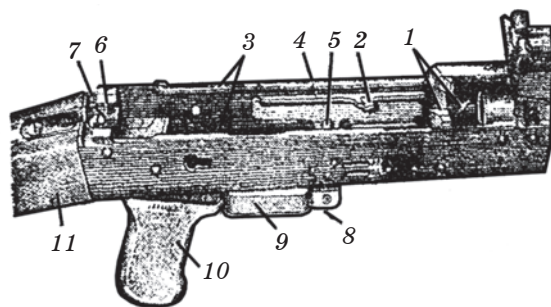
Ствольная коробка: 1 — вырезы; 2 — отражательный выступ; 3 — отгибы; 4 — направляющий выступ; 5 — перемычка; 6 — продольный паз; 7 — поперечный паз; 8 — защелка магазина; 9 — спусковая скоба; 10 — пистолетная рукоятка; 11 — приклад
